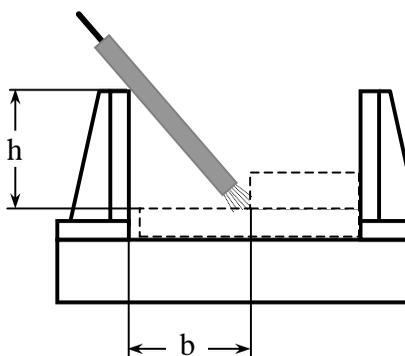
Зона доступности швов для ручной дуговой сварки
